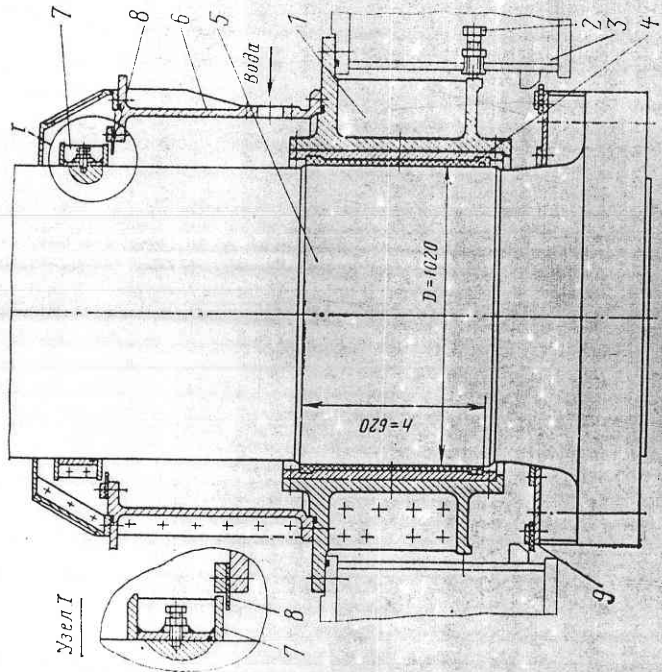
Подшипник с резиновыми вкладышами и водной смазкой
